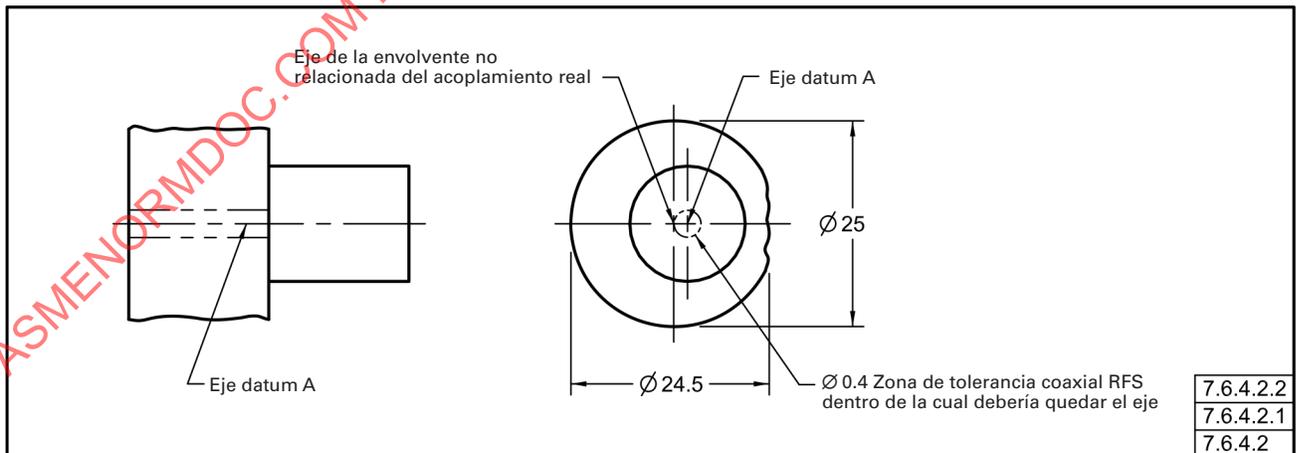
Una Posible Configuración Aceptable de la Pieza Mostrada en la Fig. 7-57
